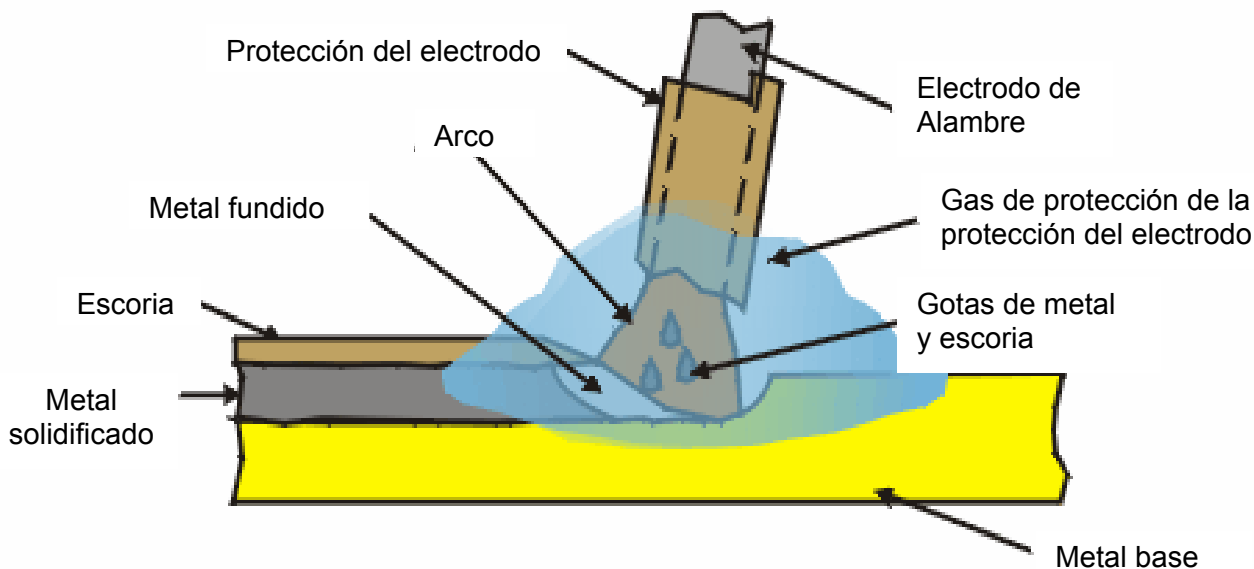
Soldadura por arco de metal protegido SMAW
